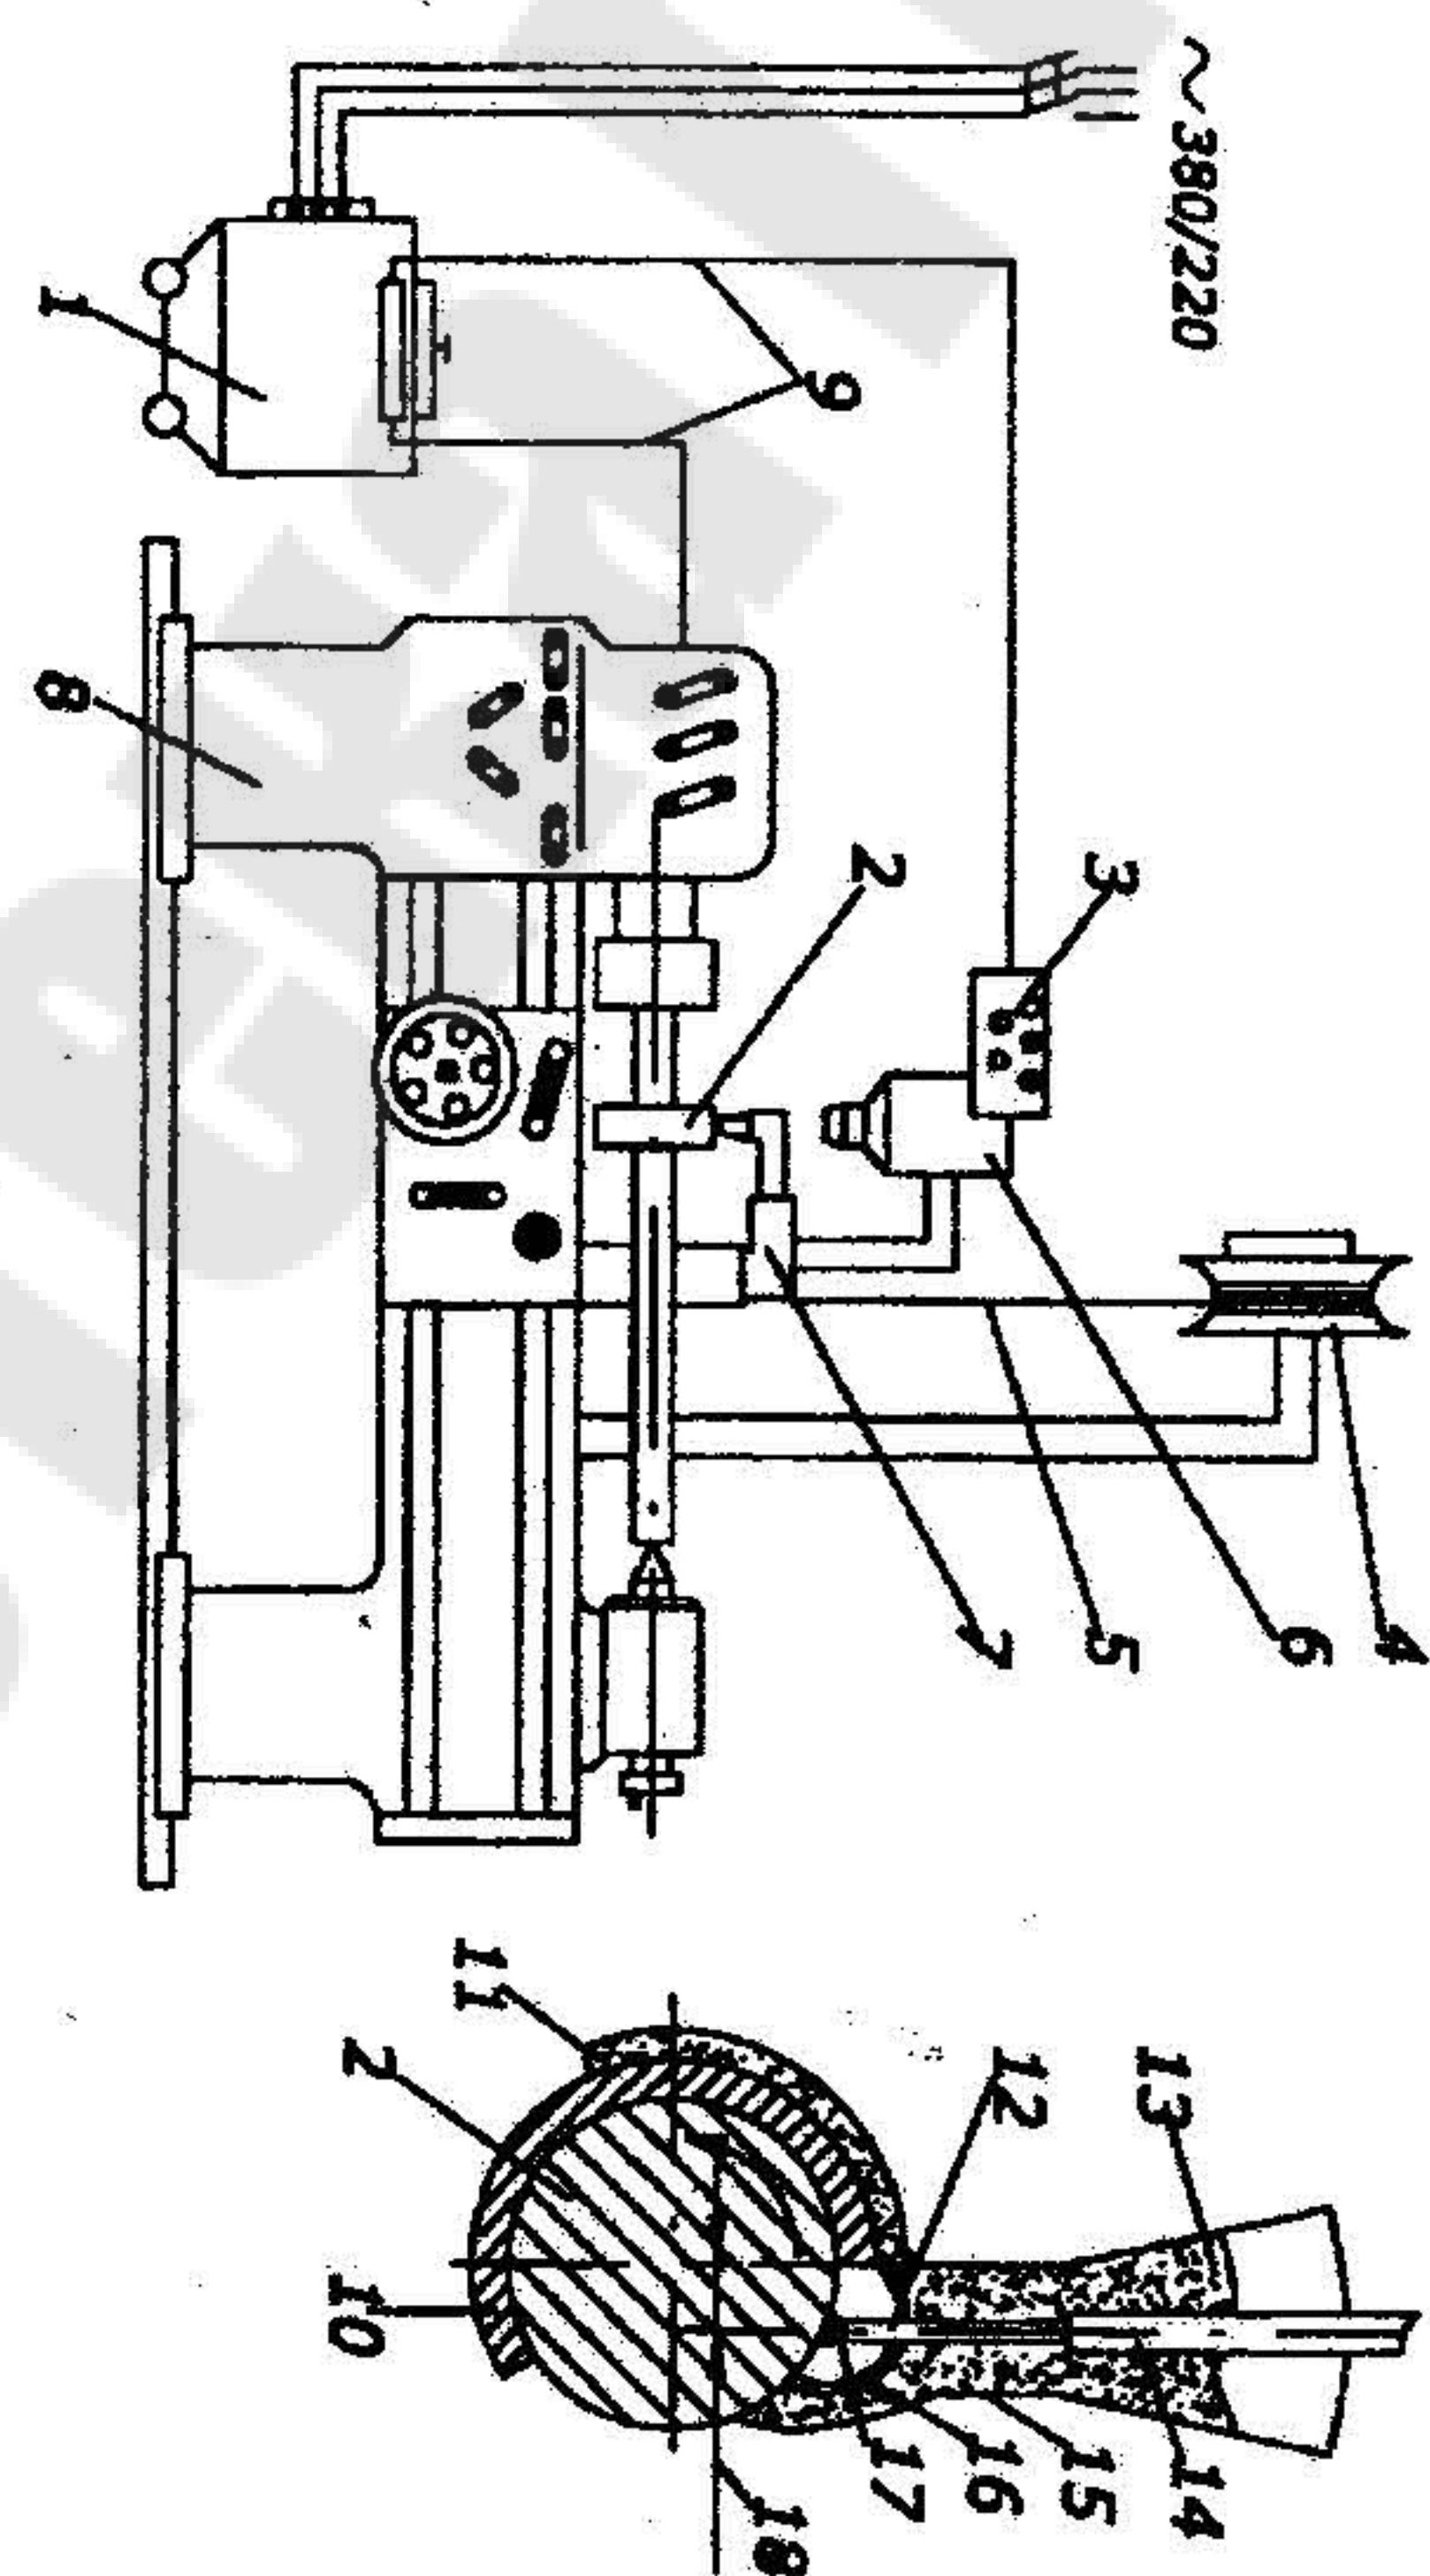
Схема установки для наплавки цилиндрических деталей под флюсом: 1 – сварочный выпрямитель ВС-600;
